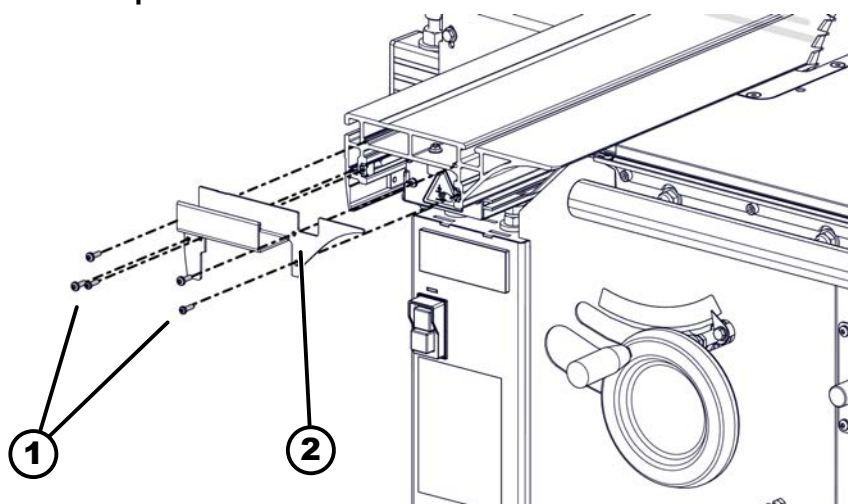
Montaje de la unidad de empuñadura del carro deslizante
